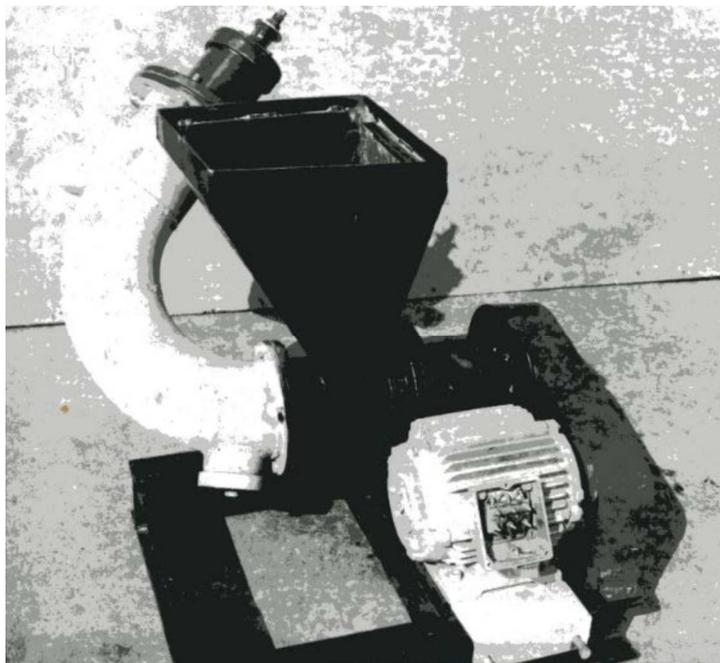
Общий вид опытного образца пружинного питателя-дозатора
